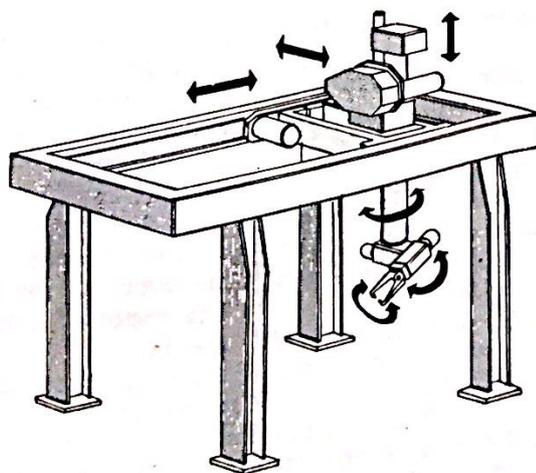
Il robot di saldatura SIV « Deltix 6 ».
